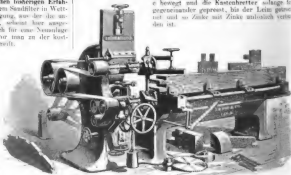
Universal-Zapfenschneldmaschine, System Fay.
